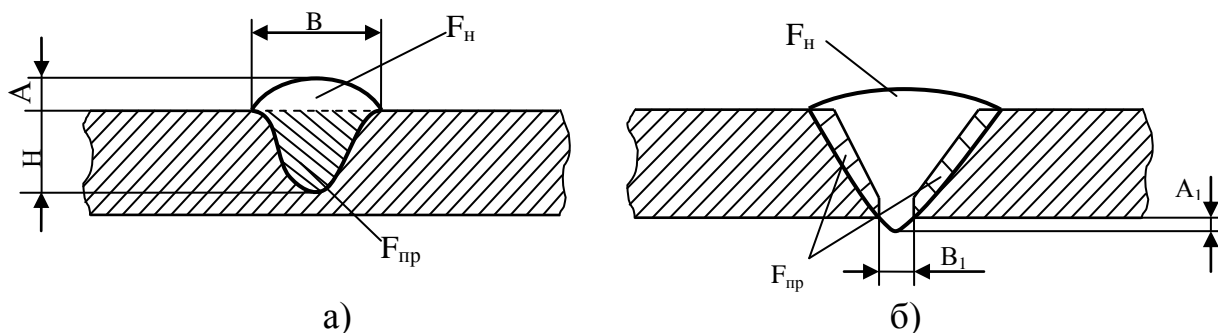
Основные параметры сварного шва: а) наплавленный валик; б) стыковой шов
